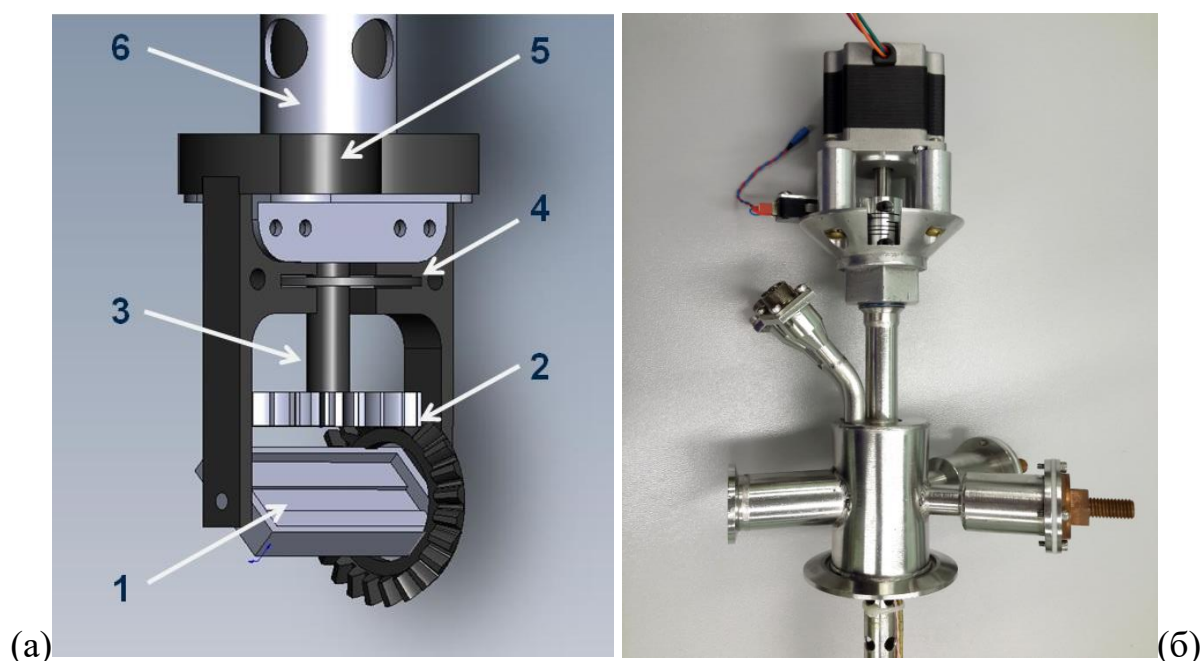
(а) – схема держателя образца с вращательным механизмом: 1) площадка крепления образца (латунь), 2) механизм вращения, 3) ось, 4) центрирующая шайба, 5) отверстие прохода хладагента, 6) несущая трубка вставки; (б) – фото верхней части вставки с установленным шаговым двигателем.
